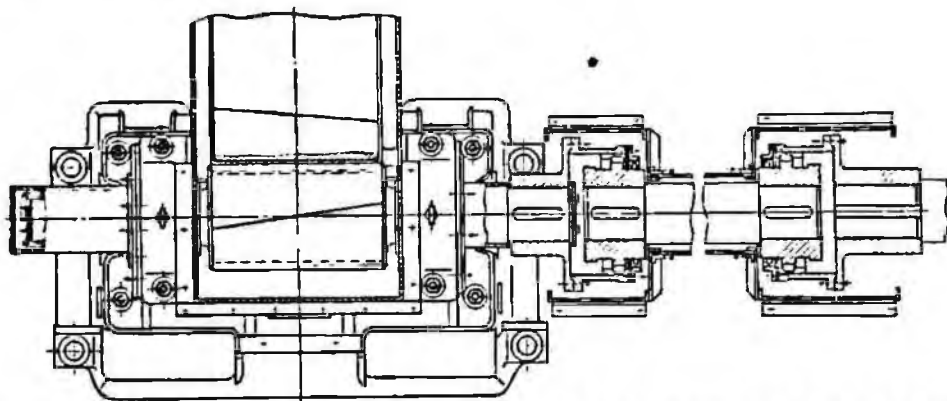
Привод шаровых и стержневых мельниц с промежуточным валом и муфтами типа МЗП
